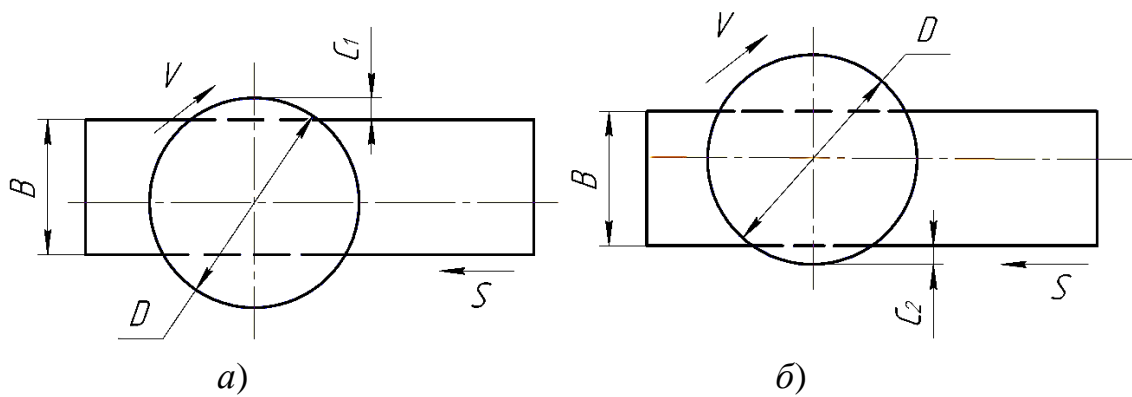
Розміщення заготовки при торцевому фрезеруванні відносно фрези: а) – врізання зуба фрези $C_1 = (0,003-0,005)D$; б) – вихід зуба фрези при $C_2 = 0$.
